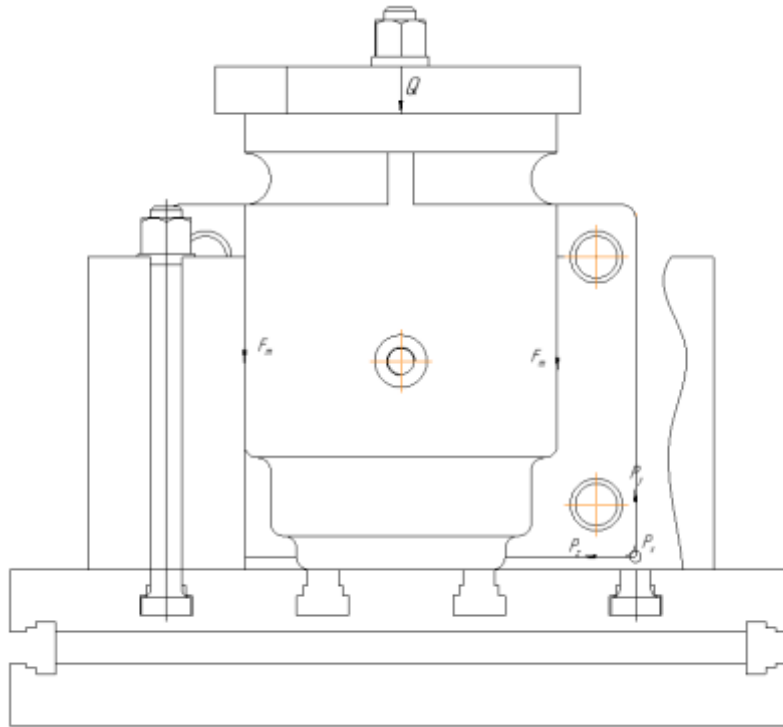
Сили які діють на заготовку на операції 005 при торцевому фрезеруванні
